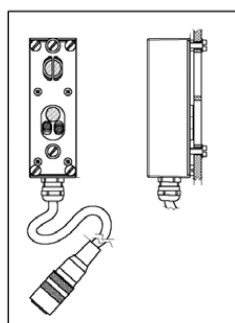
Sensore con cavo fisso. Fixed cable sensor.
